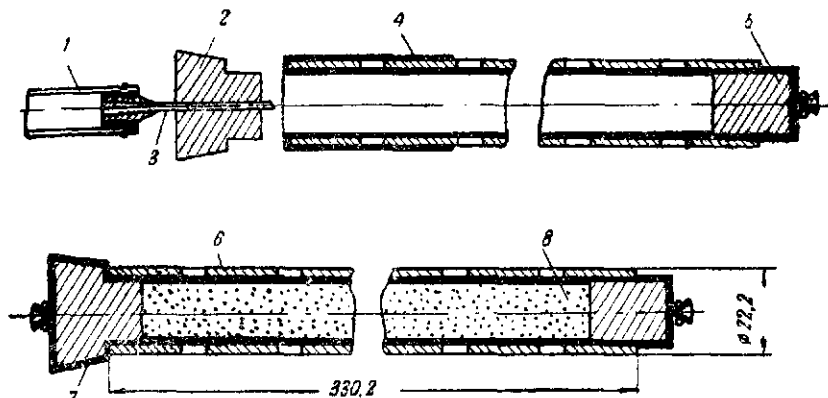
Схематический эскиз матрицы (трубки) для гидростатического прессования цилиндрических образцов. Вверху — трубка открыта для заполнения порошком; внизу — трубка собрана для прессования: 1 — резиновая оболочка; 2, 5 — резиновые пробки (стопоры); 3 — инжекторная игла для откачки воздуха из трубки; 4, 7 — резиновые оболочки 31,75 мм; 6 — отверстия дном. 6,35 мм в латунной трубке дном. 22,0 мм; 8 — порошок
